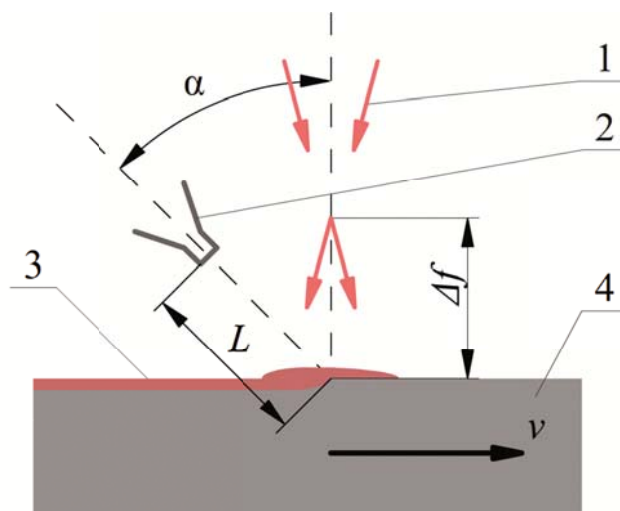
Схема газопорошковой лазерной наплавки с подачей порошка вслед движению образца:
